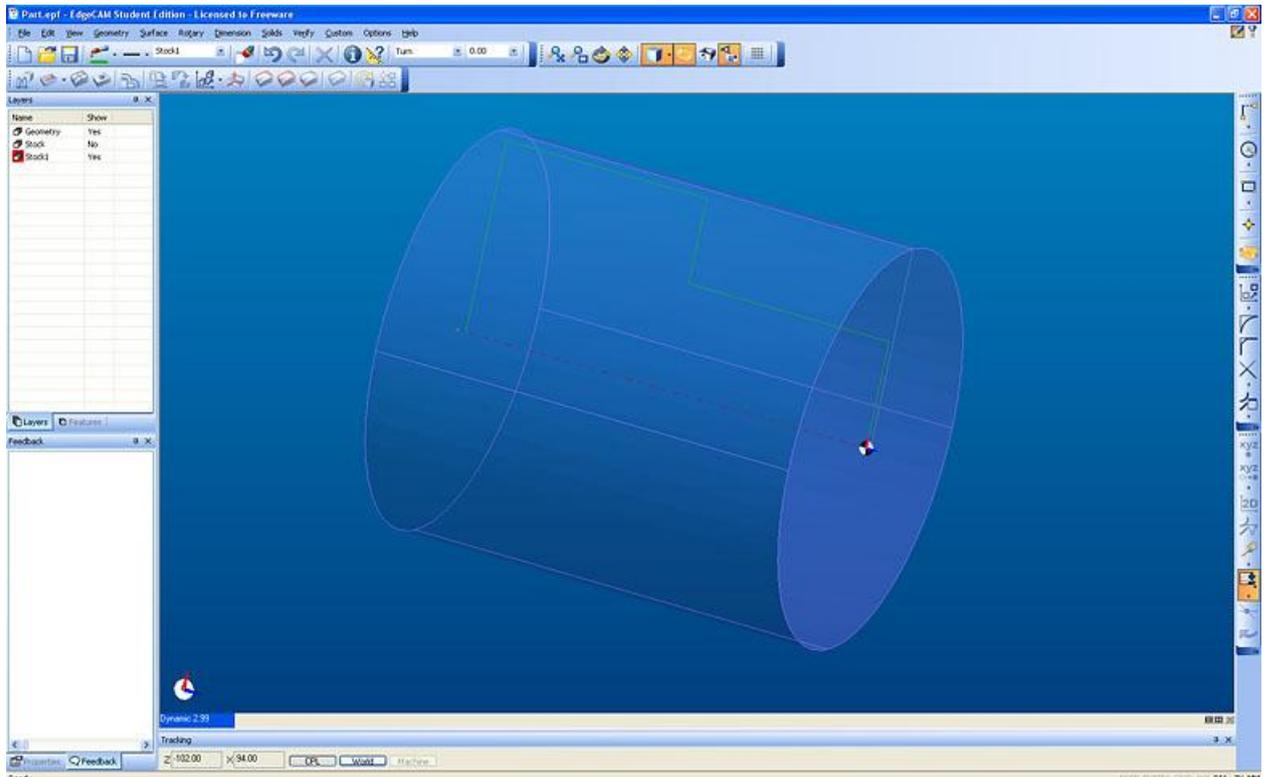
Edgescam. Создание заготовки для токарной обработки
